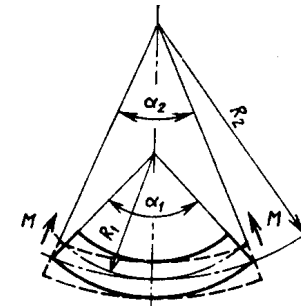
Схема пружинения изогнутой заготовки
